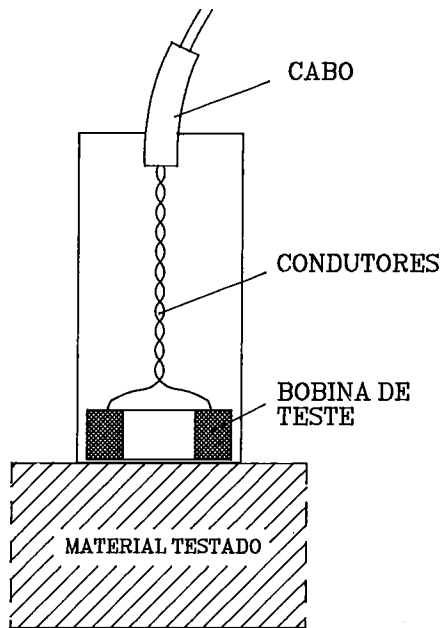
DISPOSITIVO DE ENSAIO DE UMA SÓ BOBINA
